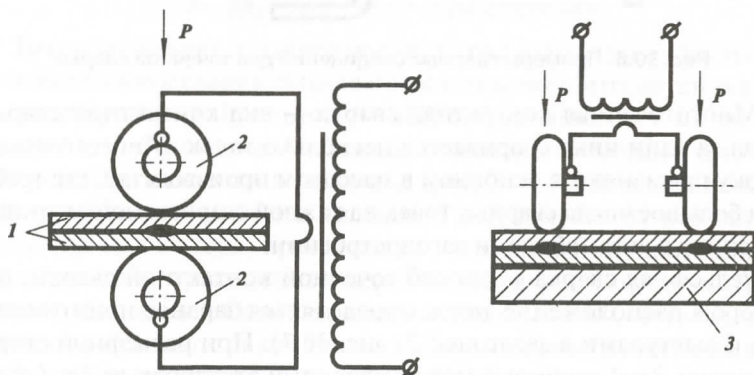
Принципиальная схема шовной сварки:
